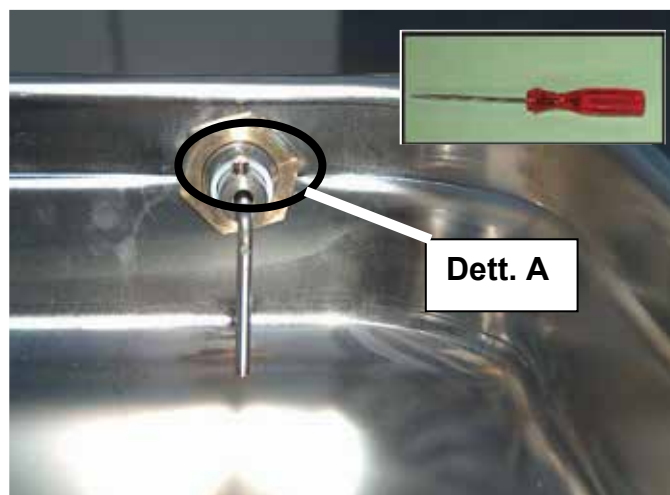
Detailansicht Füllstandssensor; fehlerhafte Montage
